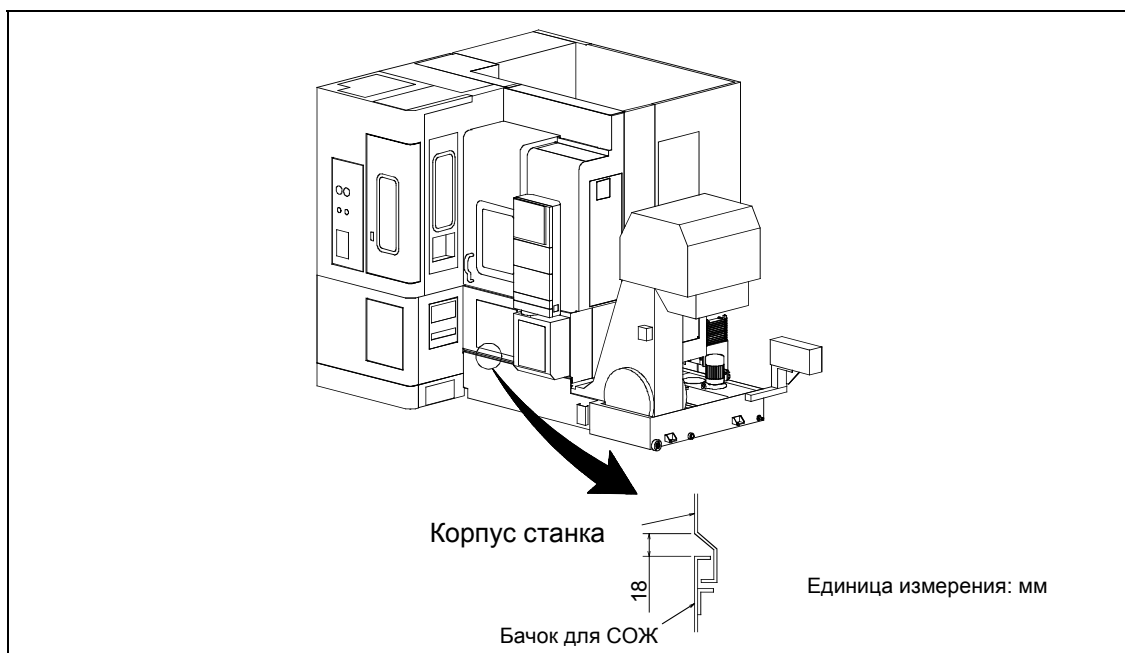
Регулировка зазора между корпусом станка и бачком для СОЖ
